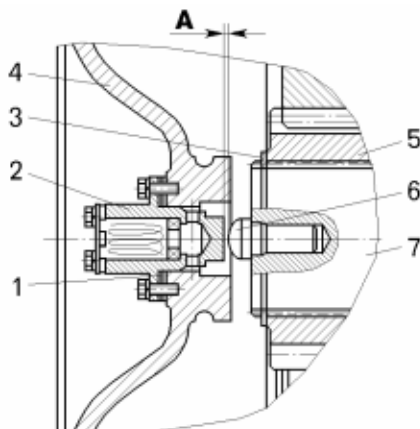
Стенд для сборки-разборки редукторов мотор-колес и регулировки подшипников второго ряда:
